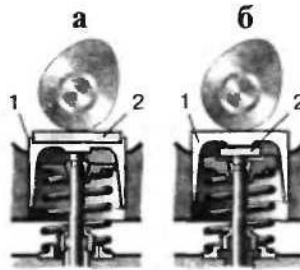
Приклади технічних рішень механізму приводу клапана з циліндричним штовхальником: а - кулачок розподільного вала натискає на поверхню регулюючої шайби; б - кулачок натискає на поверхню штовхальника, регулювальна шайба встановлена між горцем клапана і штовхальником; 1 - штовхальник; 2 - регулююча шайба
